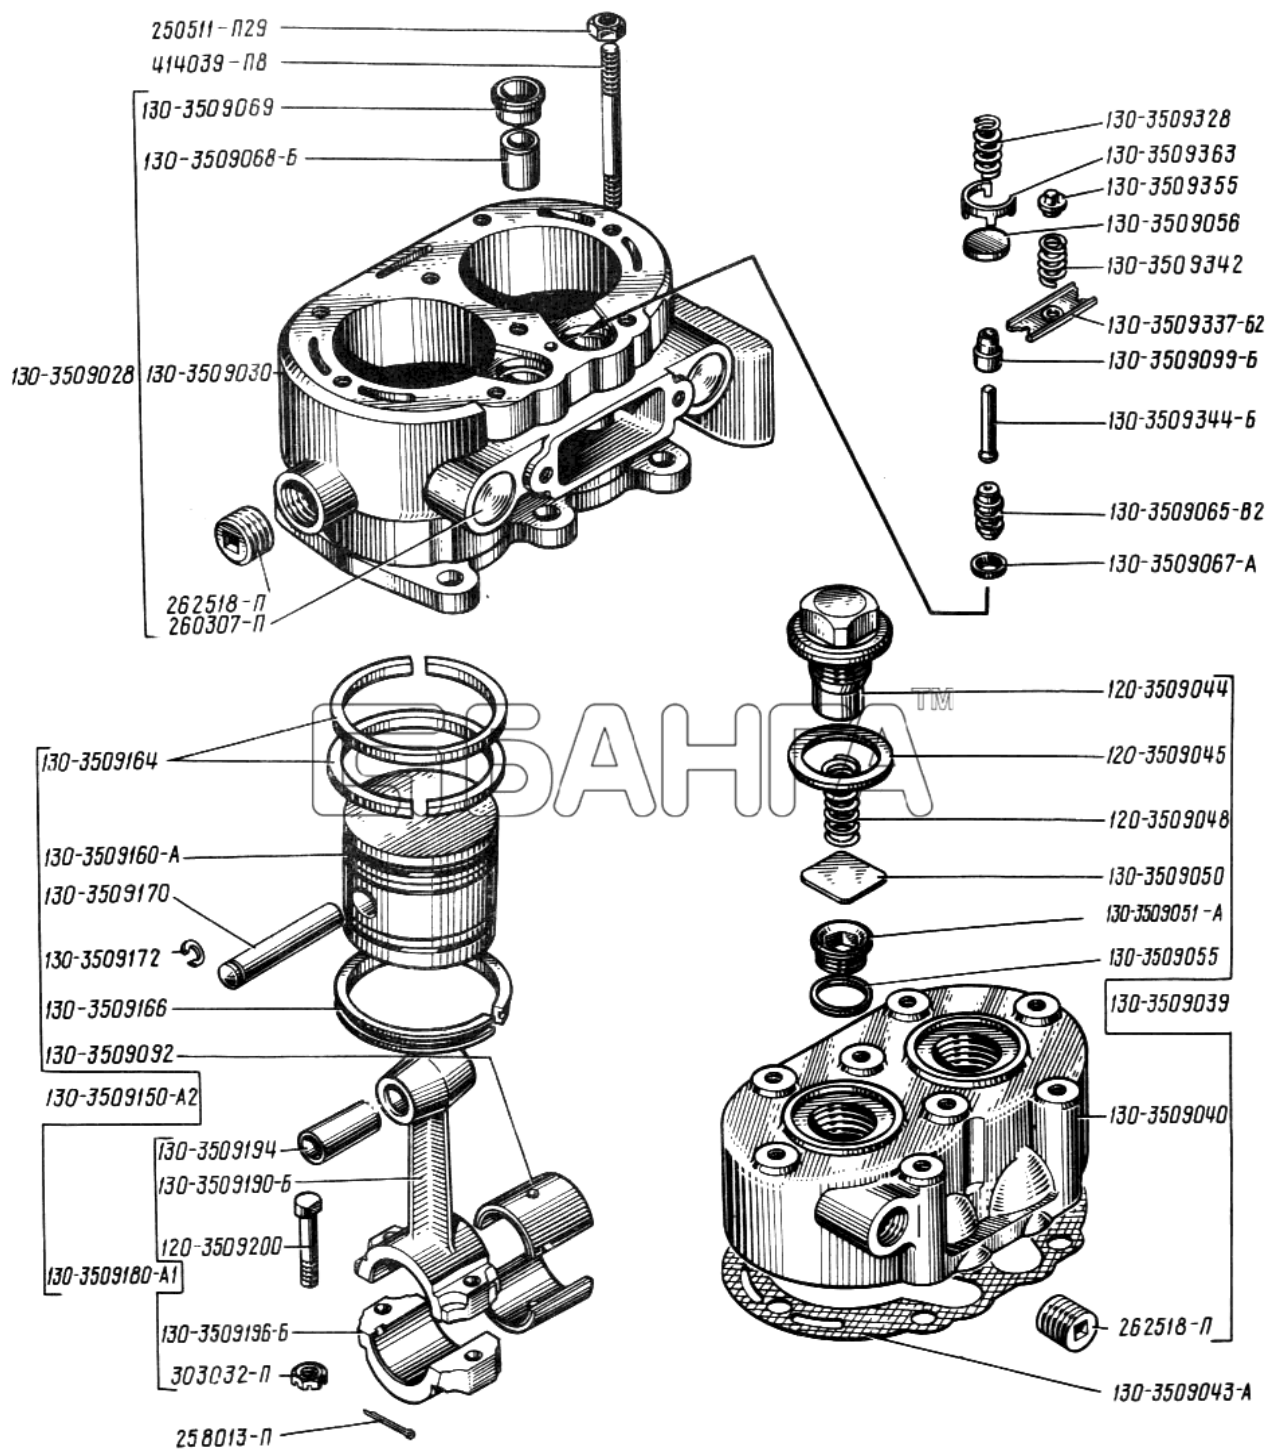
Компресор (головка і блок циліндрів)
